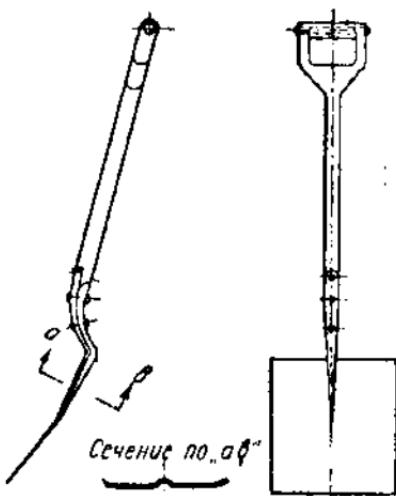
Ручное приготовление земли на месте изготовления форм.
